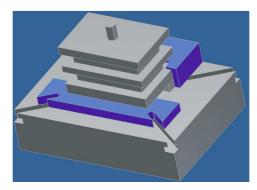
Desenho Técnico da montagem da base da prensa, cunho e calços
